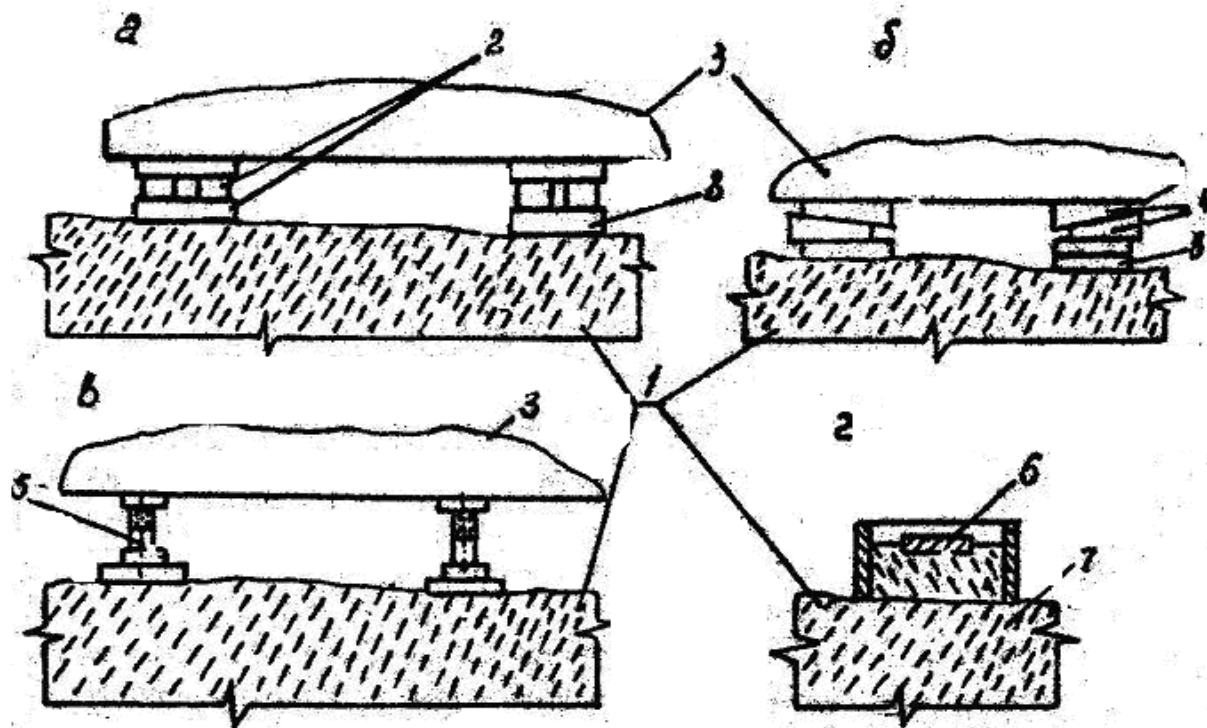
Способы отпирания оборудования (рам) на фундамент:
